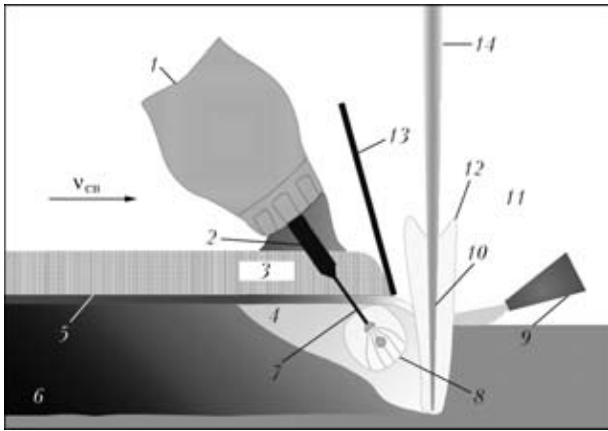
Схема гибридной лазерно-дуговой сварки под флюсом: 1 — бункер для флюса; 2 — контактная трубка; 3 — флюс; 4 — жидкая ванна; 5 — твердый шлак; 6 — металл шва; 7 — проволочный электрод для дуговой сварки под флюсом; 8 — полость шва с дугой; 9 — струя гелия; 10 — парогазовый канал; 11 — жидкий шлак; 12 — плазма с парами металла; 13 — разделительная пластина; 14 — лазерный луч
